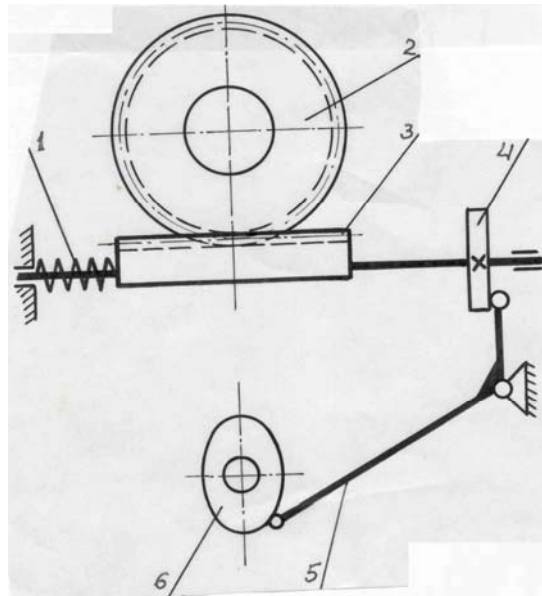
Схема механізму перетворення обертового руху у зворотно-обертовий
